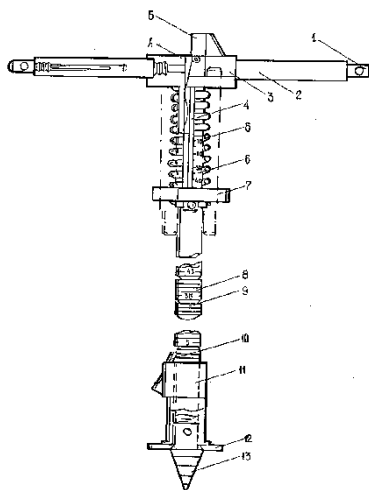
Ручний пенетрометр РП-1: 1 – ключ; 2– ручка; 3 – рухома головка; 4 – напрямна шпилька; 5 – калібрована пружина; 6 – шкала зусилля втискування; 7 – опора пружини; 8 – штанга; 9 – кільцева проточка; 10 – клямка; 11 – показчик глибини вдавлювання; 12 – опорна плита; 13 – наконечник; А – площина ступінчастого зрізу, для зусилля 200 Н; Б – площина для контролю зусилля 400 Н
